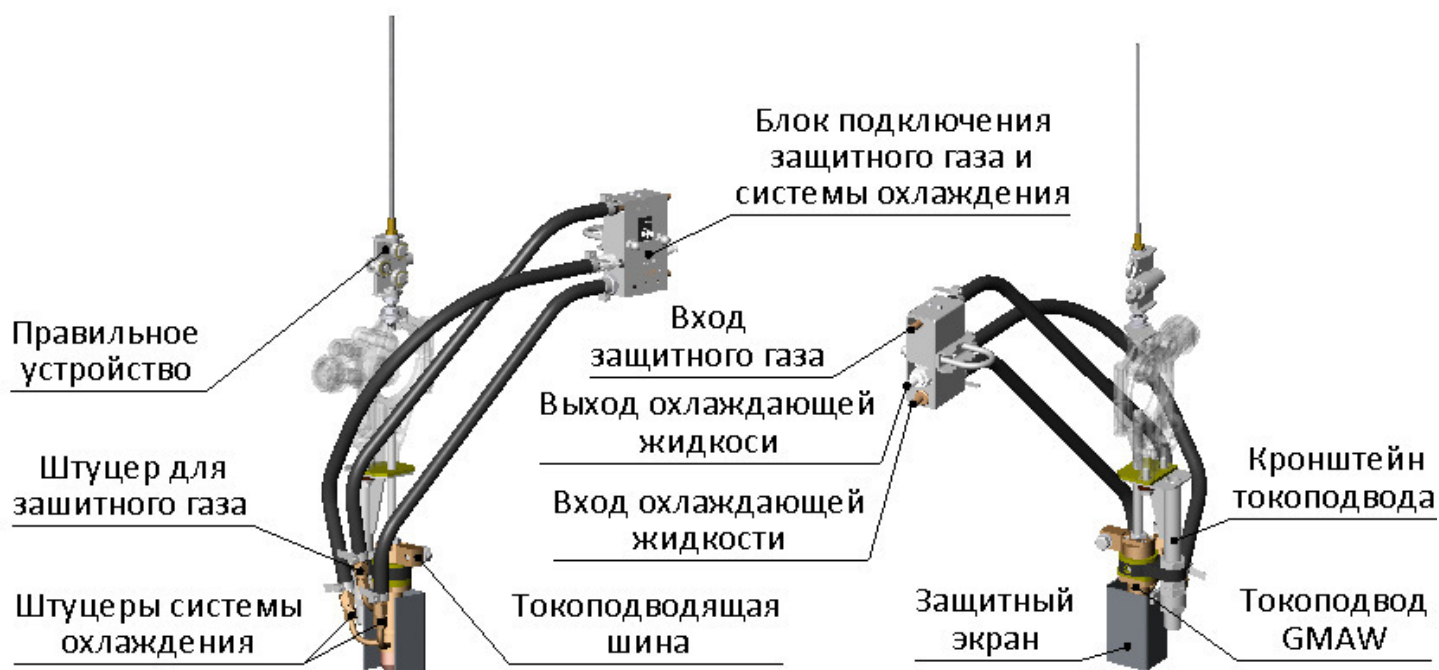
Комплект токоподвода для сварки GMAW.
